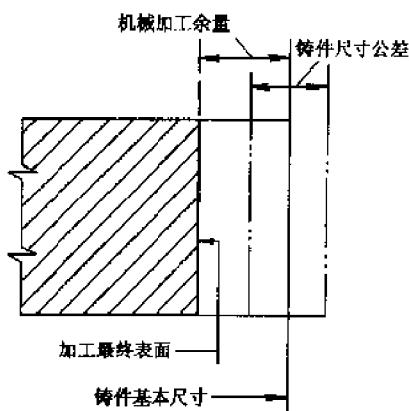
铸件基本尺寸与机械加工余量及铸件尺寸公差的关系
